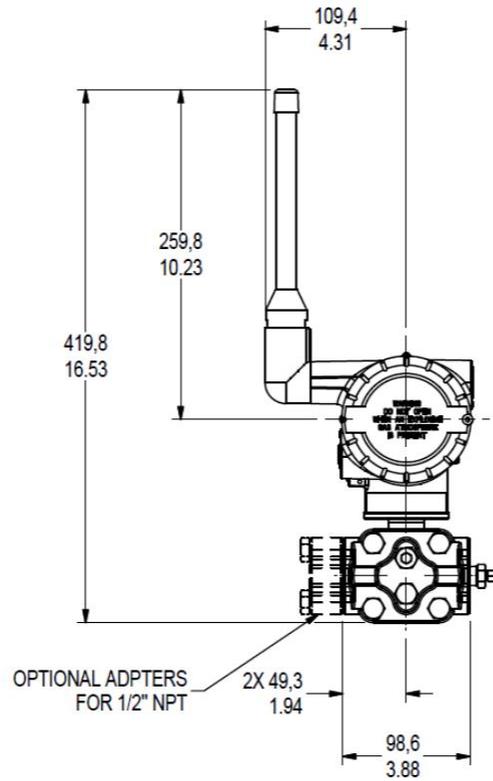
Jauge à deux têtes, , dimensions de montage typiques pour STGW740, STGW770 (antenne 4 dBi montrée, vue arrière)
